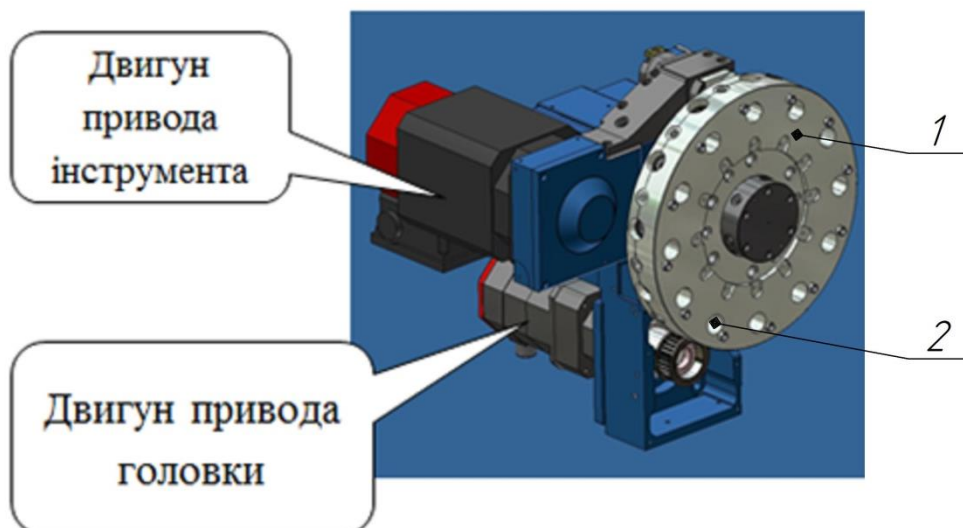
Револьверна головка з двигуном приводу головки та інструменту
